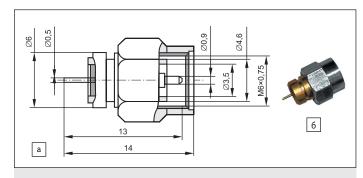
Соединитель ТС2.236.074: а) конструкция; б) внешний вид
